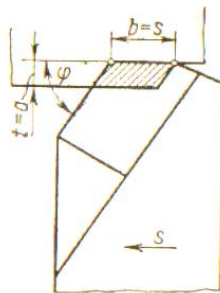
Чистовой резец с комбинированной заточкой (резец Колесова)
